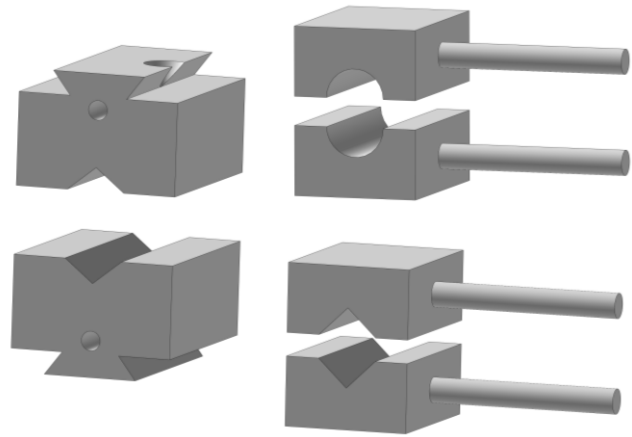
Virіzni бойки для протягування заготовок круглого перерізу
